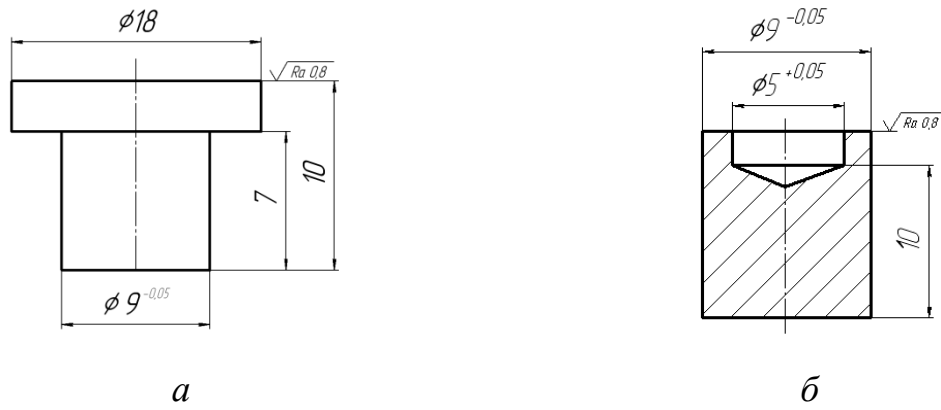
Робочі креслення зразка (а) та контрзразка (б) для досліджень на фретинг-зношування
